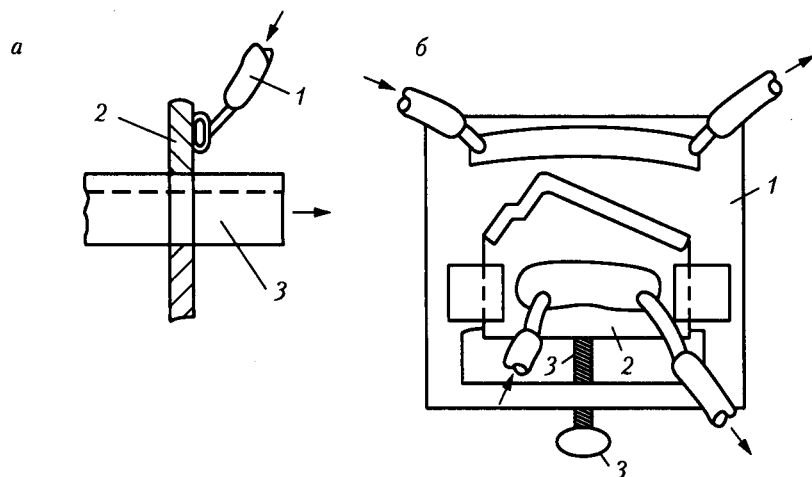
Конструкция калибрующей пластины для калибрования профиля.
